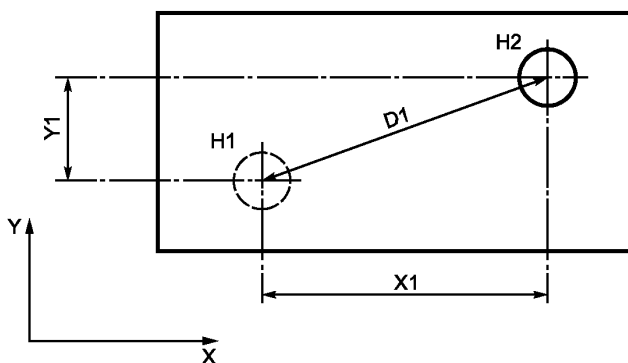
Установочный и присоединительный размер с измеряемым отрезком
